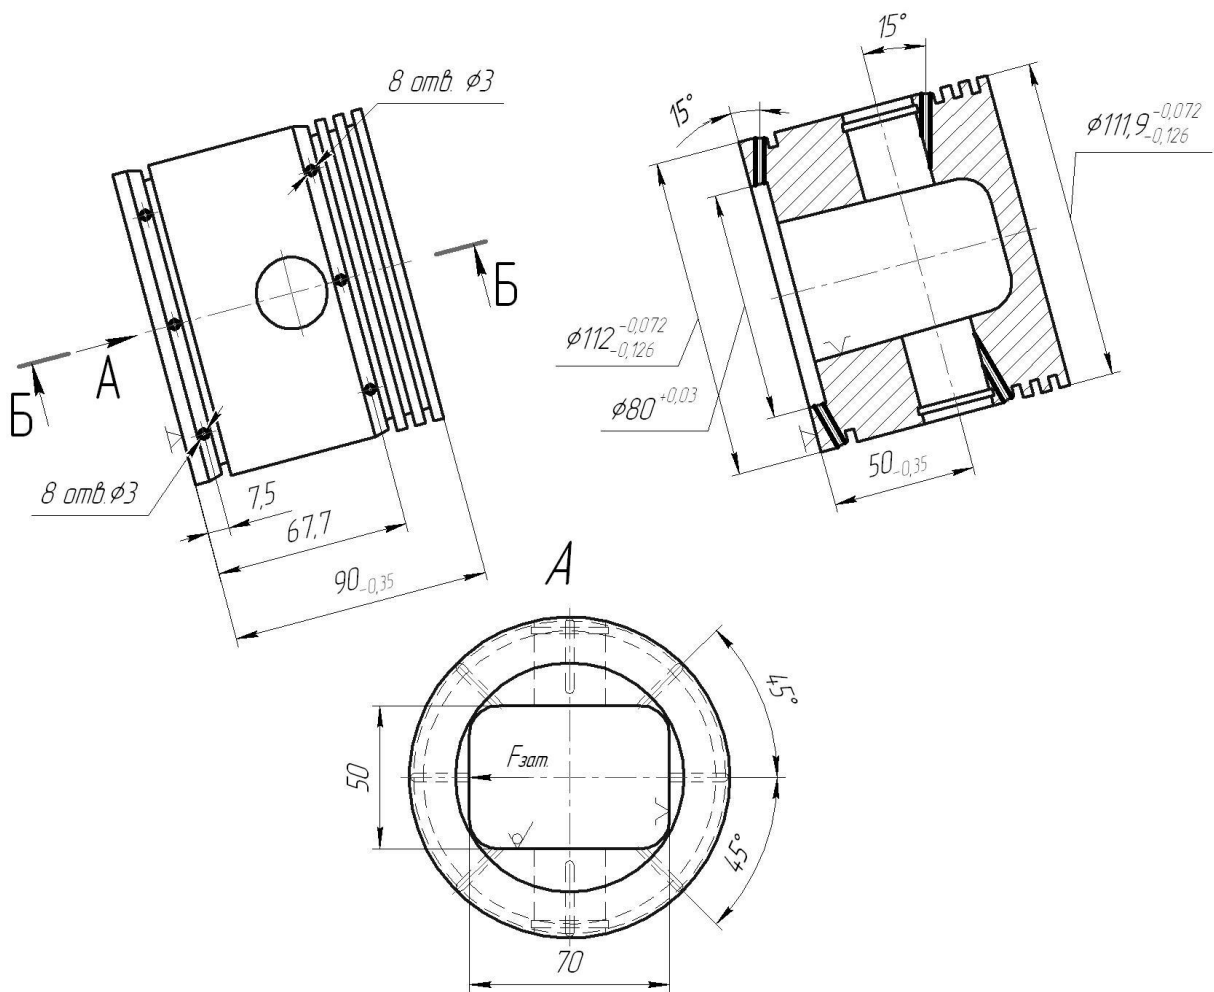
Ескіз механічної обробки деталі поршень компресора
